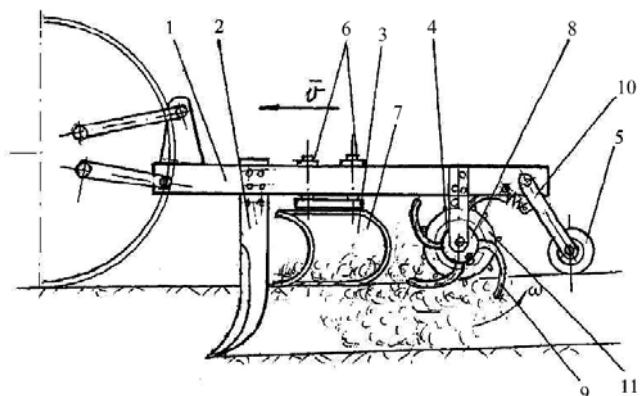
Комплексный почвообрабатывающий агрегат [5]: 1 – рама; 2 – щелерез; 3 – соломонаправитель; 4 – соломозаталкиватель; 5 – каток; 6 – болтовые соединения; 7 – полуцилиндрический отвал; 8 – шайба; 9 – пружинные пальцы; 10 – рама катка; 11 – приводное колесо со шпорами
